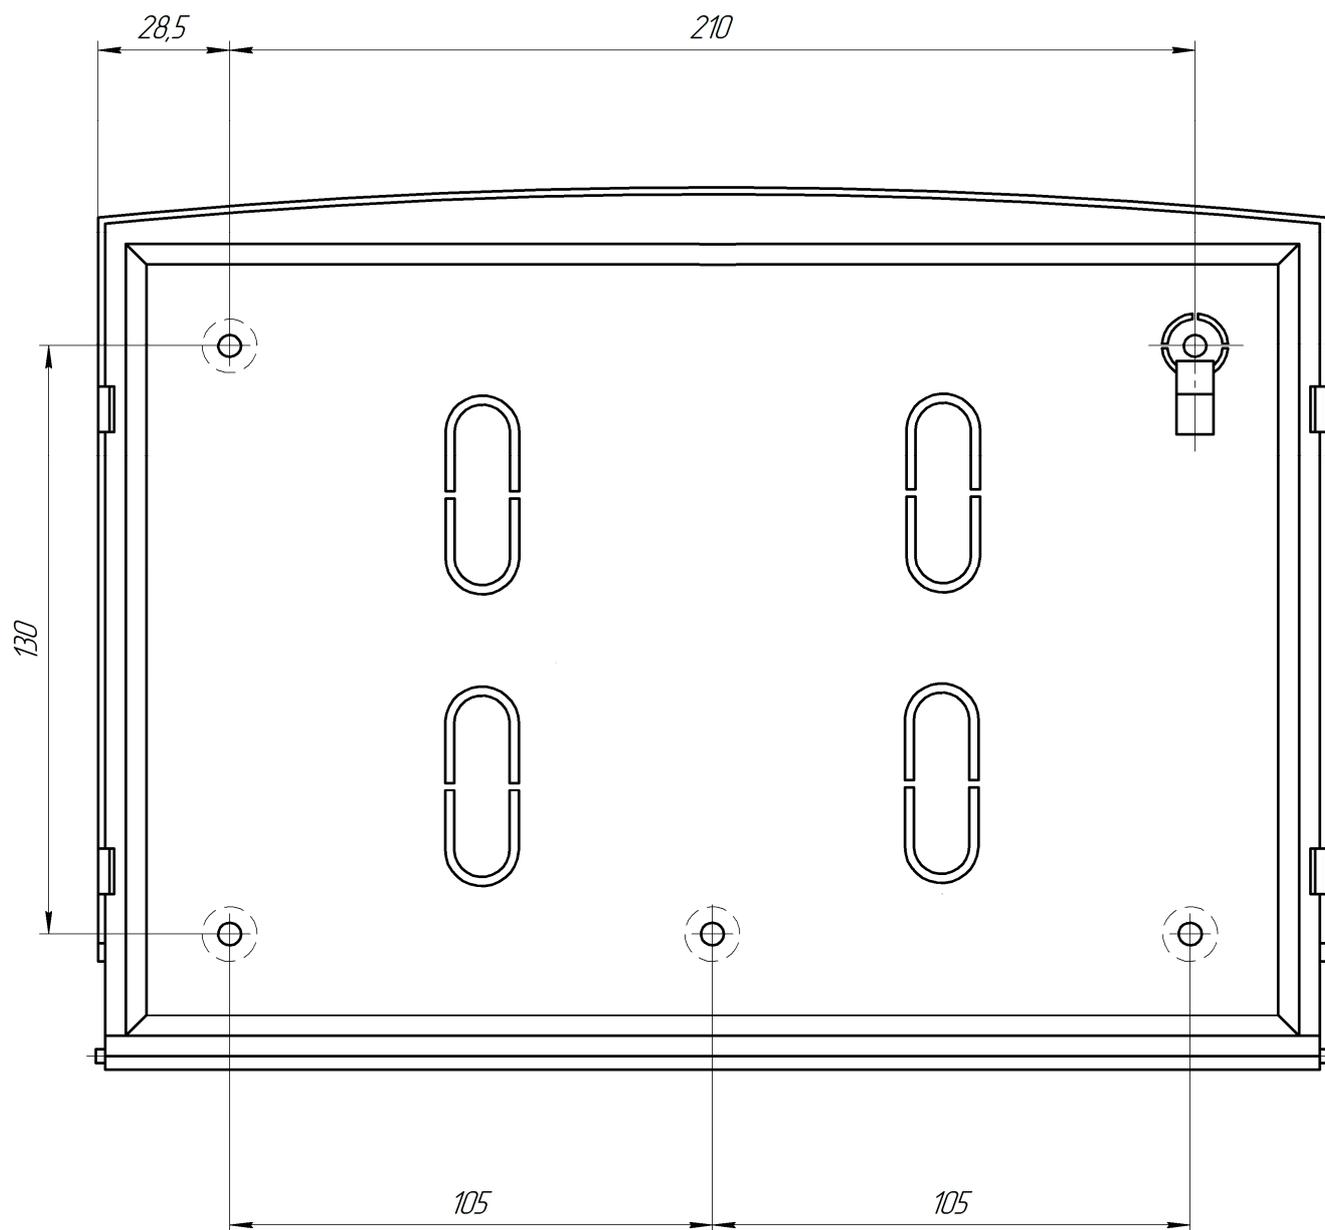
Разметка отверстий для крепления прибора.
